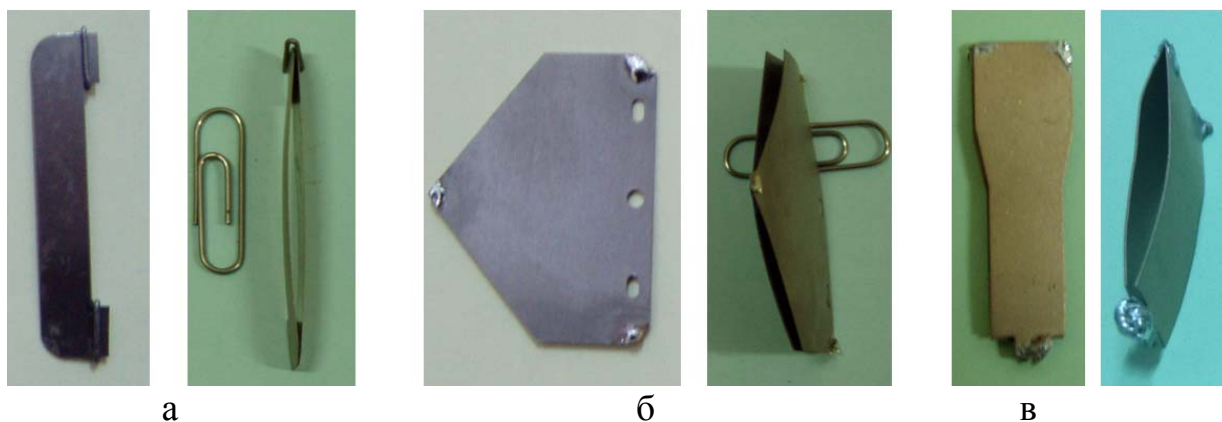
Зовнішній вигляд спарених деталей до й після абразивної обробки затопленими струменями: а – титановий сплав ВТ-1; б – сталь 65Г; в – берилієва бронза БрБ2
